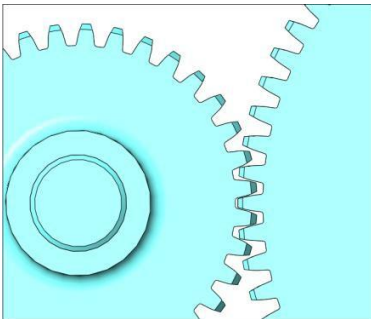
Орієнтація зубів шестерні й колеса
